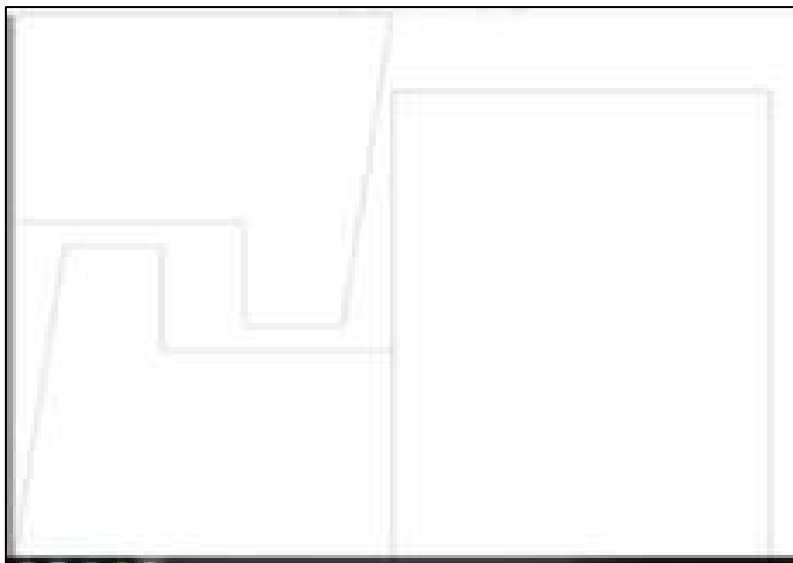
Diseño en Corel para corte laser, parte derecha e izquierda
